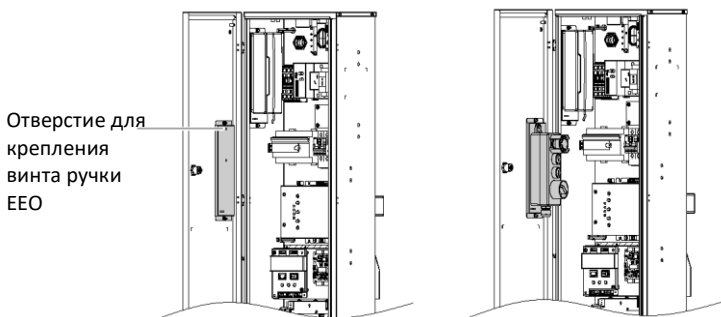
Установка ручки ЕЕО шкафа управления MRL (пожарный лифт)
